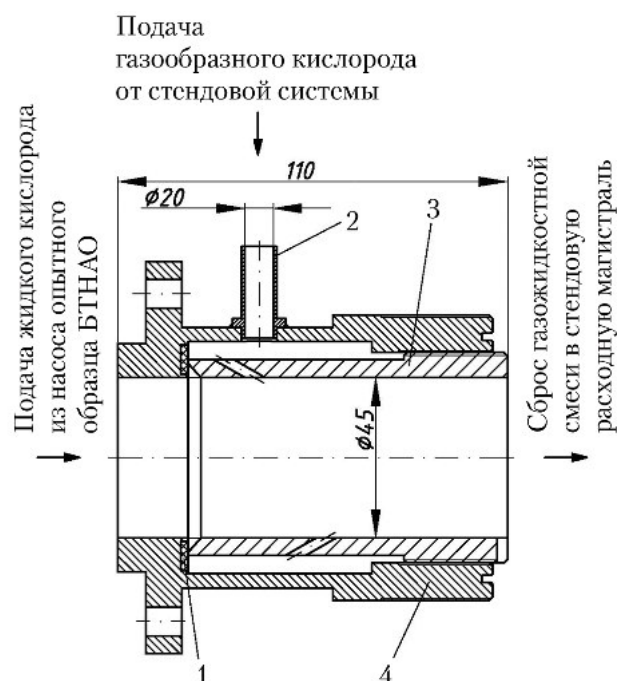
Общий вид струйного насоса-конденсатора: 1 — уплотнительное кольцо; 2 — трубка; 3 — вставка; 4 — корпус
